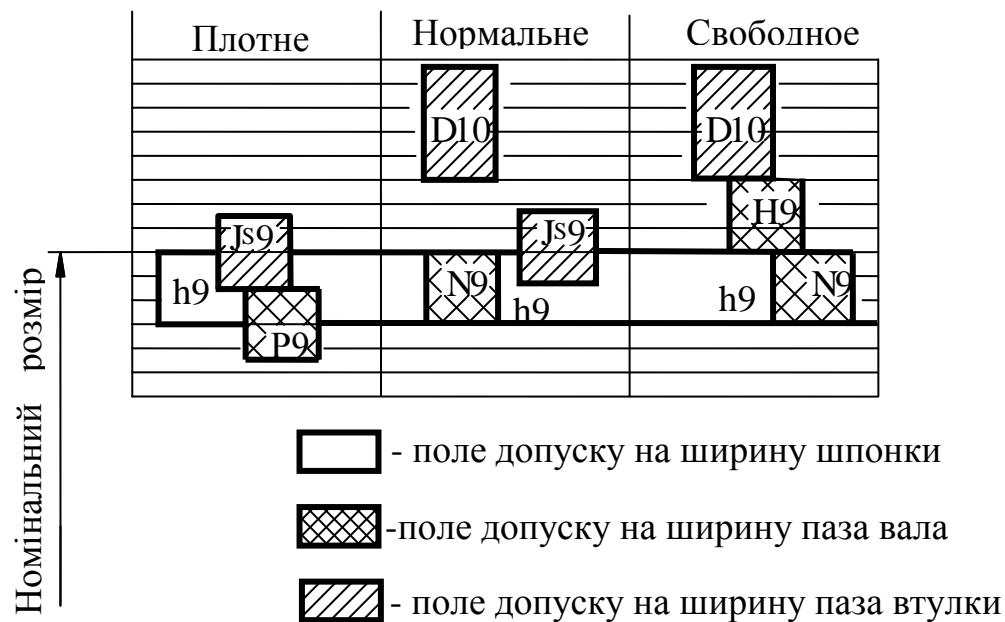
Схема полів допусків шпонкового з'єднання
